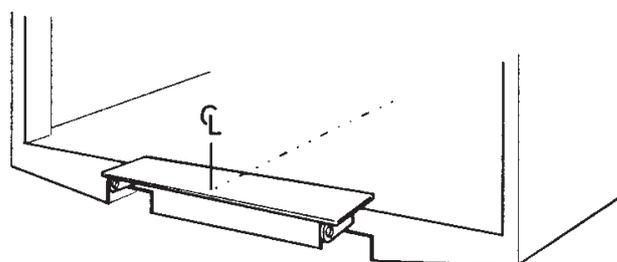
Schrauben oder punktschweißen der Montagevorrichtung an der Hecktraverse. Art.Nr 51724
